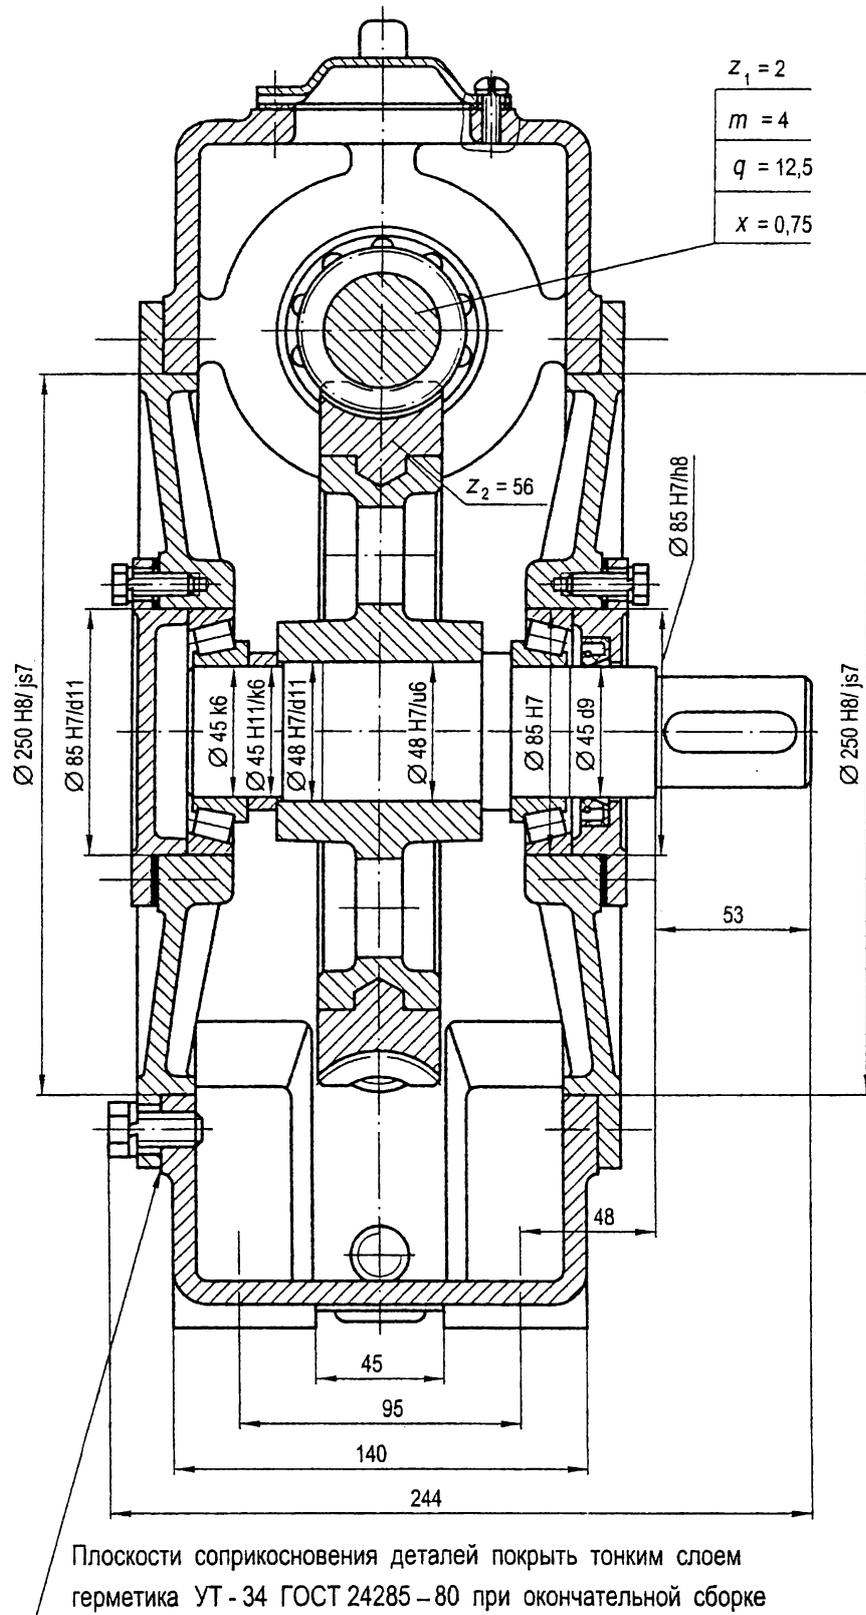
Тихоходный (выходной) вал редуктора с червячной передачей (червяк расположен горизонтально над червячным колесом)
